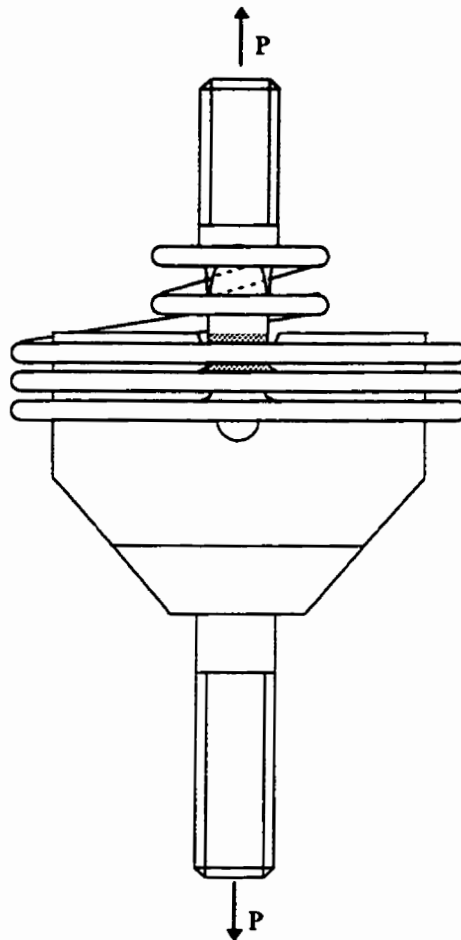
Éprouvette, mors inférieur et bobine d'induction
